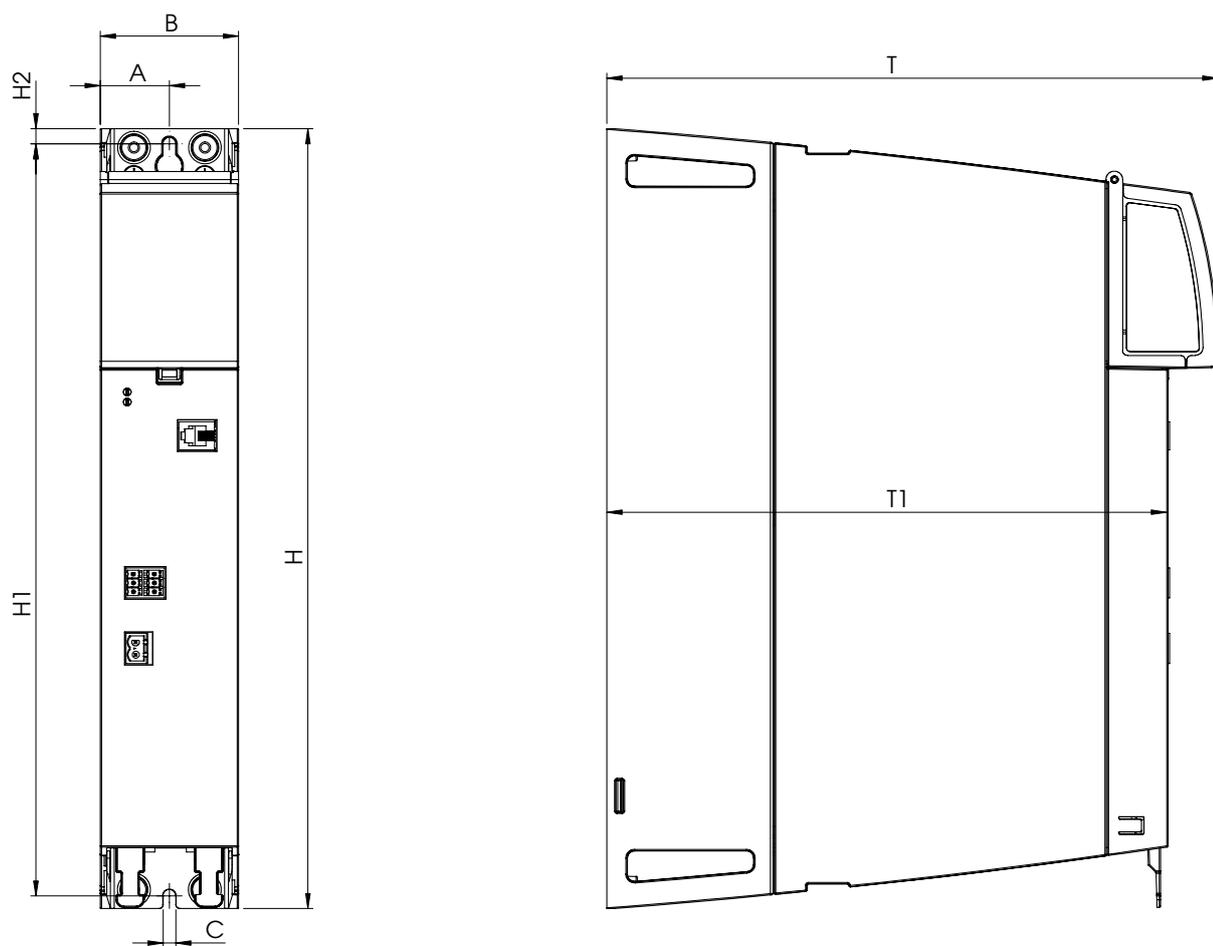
JM-3000 电源装置 BG1 尺寸图（尺寸请参见表表 2.1）
